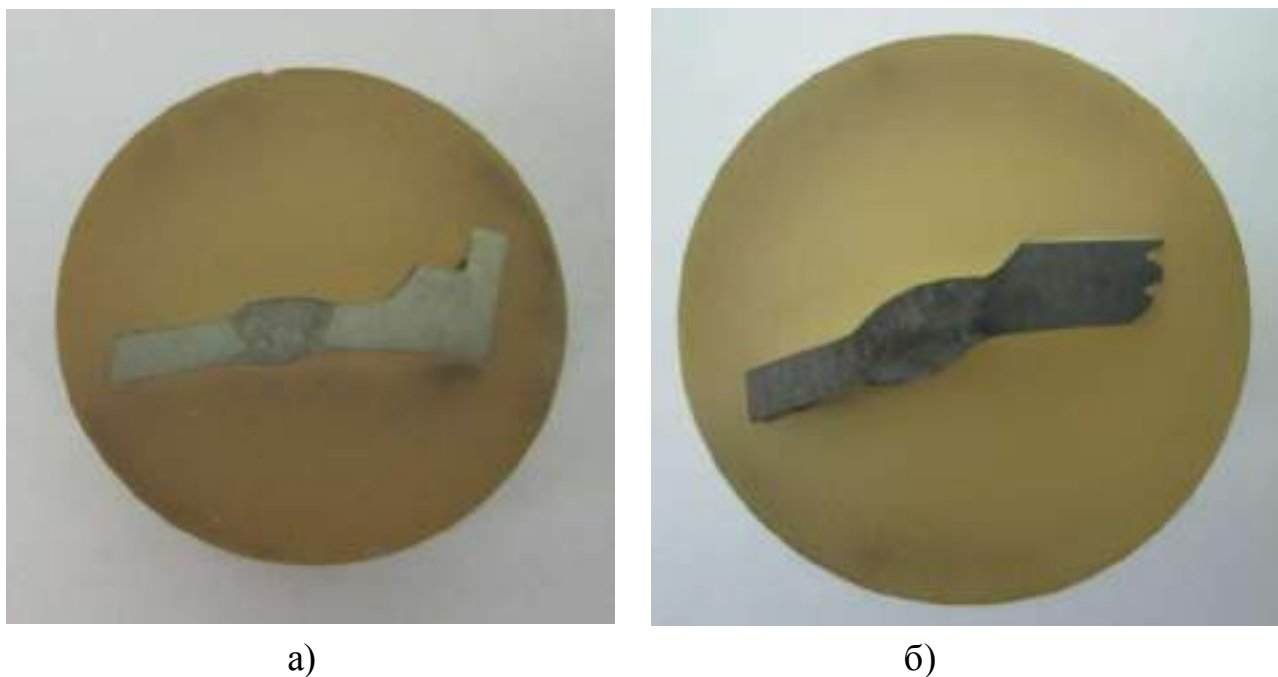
Образец сварного шва: а) – до термообработки; б) – после термообработки
